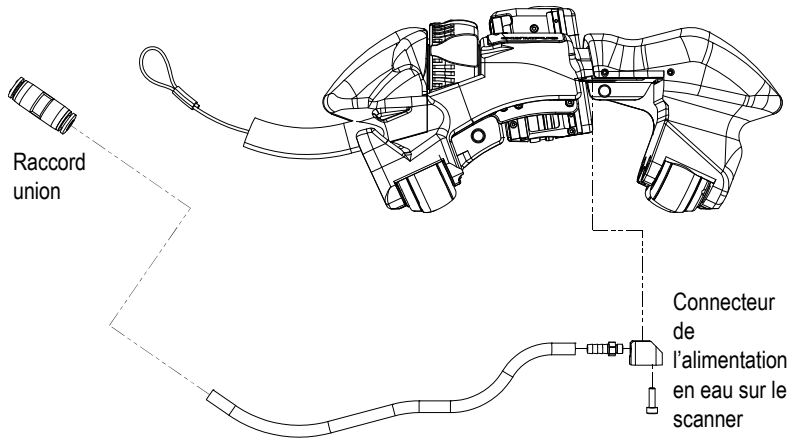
Remplacement du tube d'alimentation en eau (désassemblé)
